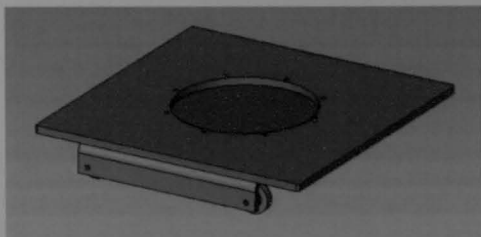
33 - Estrutura de deslocação da caixa de moldação.
